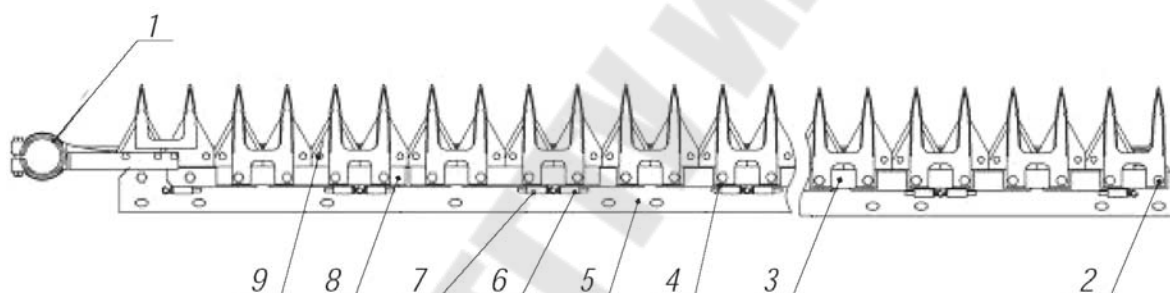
Конструктивная схема режущего аппарата жатки:
